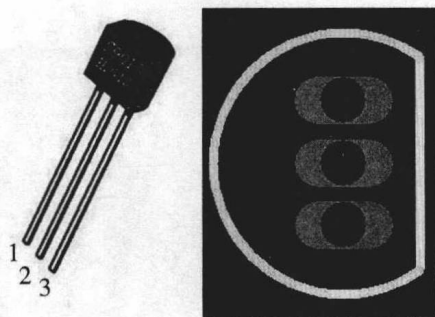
穿孔安装式封装的元件外形及其PCB焊盘
